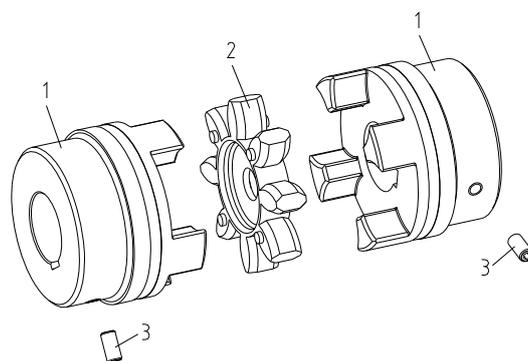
ROTEX® GS, типоразмеры 42 - 75
